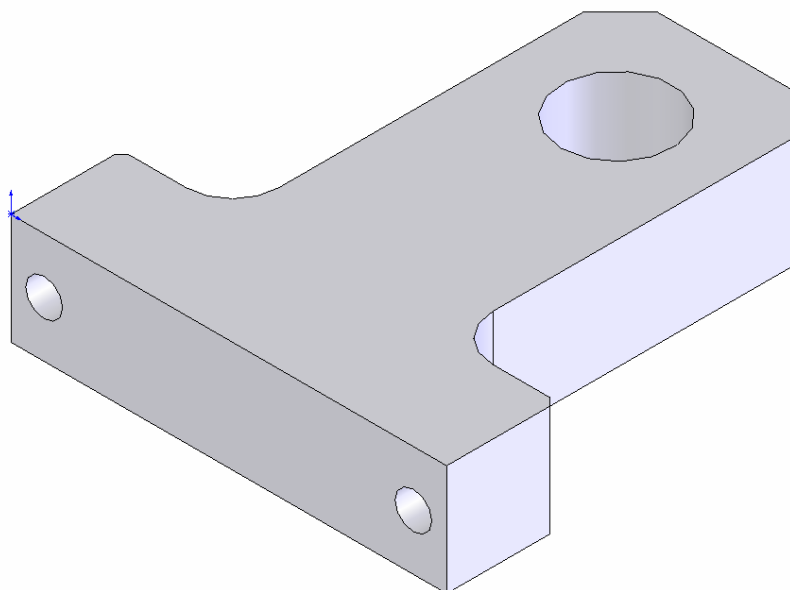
Dibuix en tres dimensions de la peça 2; suport rodillo. Solidworks ®
